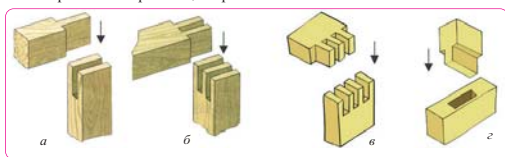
Виды шиповых соединений: а – открытое одинарное, б – открытое двойное; в – открытое тройное; з – прямое закрытое
